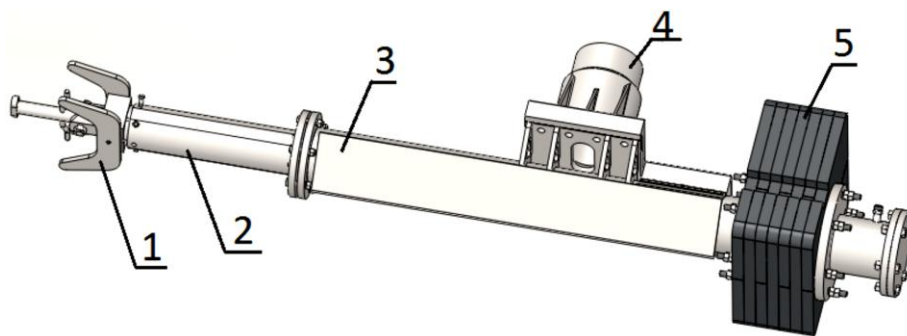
Базова конструкція маніпулятора: 1 – затискач; 2 – шток; 3 – корпус; 4 – привідний вал маніпулятора; 5 – противага
